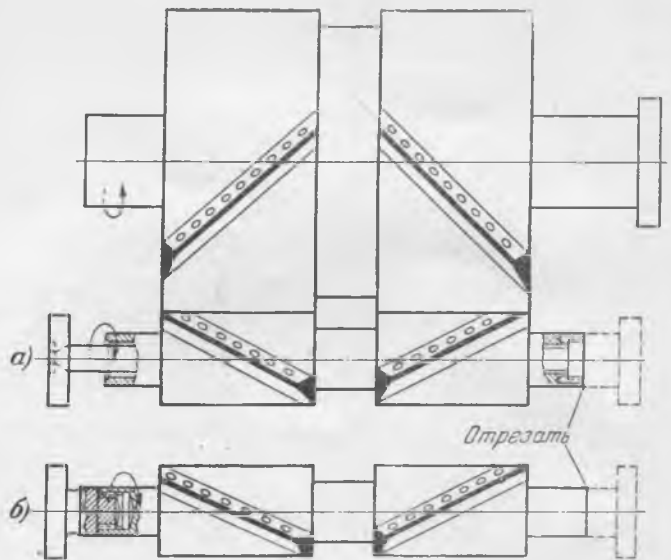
Перенасадка зубчатых венцов колеса и запрессовка их на противоположные ступицы с поворотом на 180°. а — поворот шестерни и передка ее на торсионный вал; б — наделка полумуфты после поворота шестерни.
